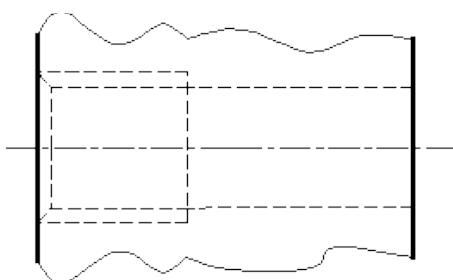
Изображение цилиндрической резьбы в отверстии
